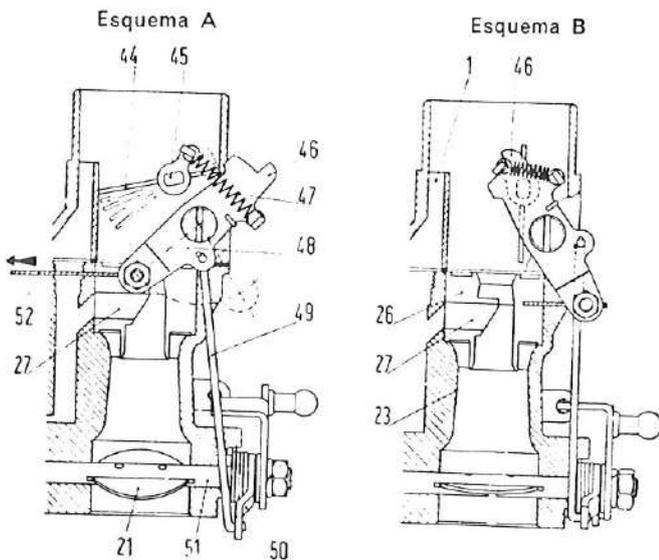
Secciones del carburador Bressel tipo 28 ICP 6.
